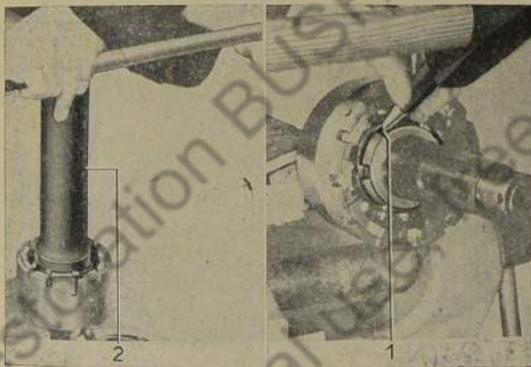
Nutmutter für Antriebskegelrad abschrauben
